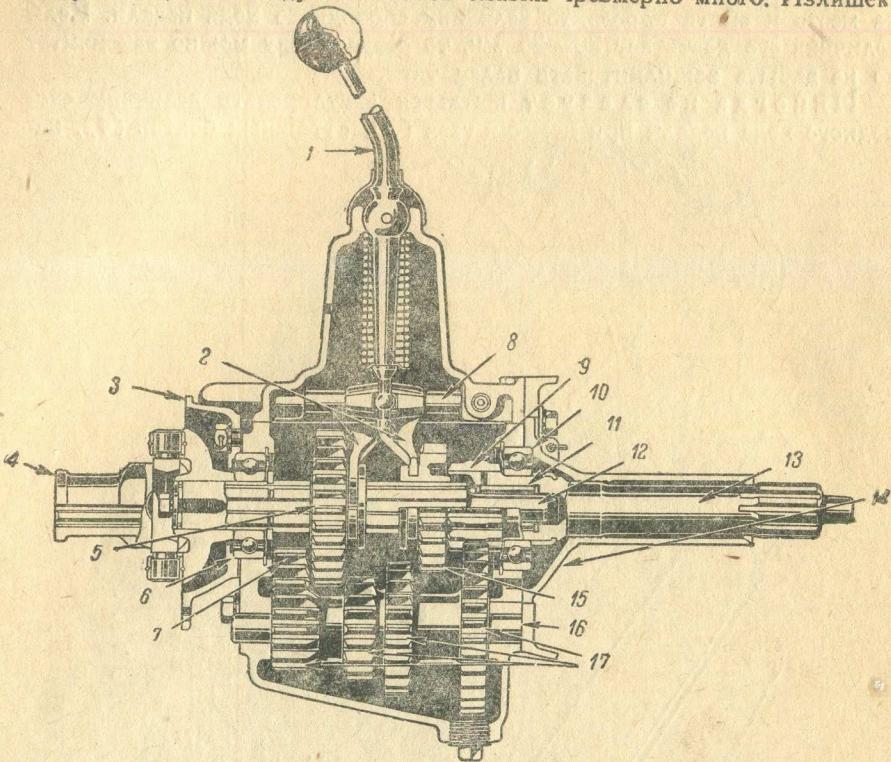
Коробка передач автомобиля ГАЗ-А.
